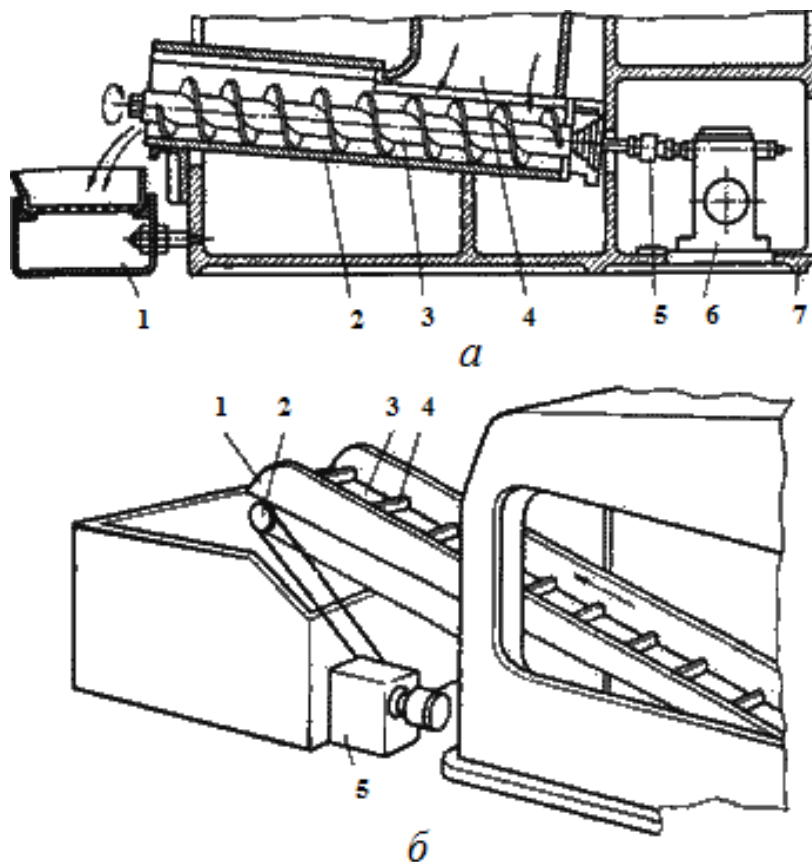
Конвеєри для видалення стружки з верстатів
